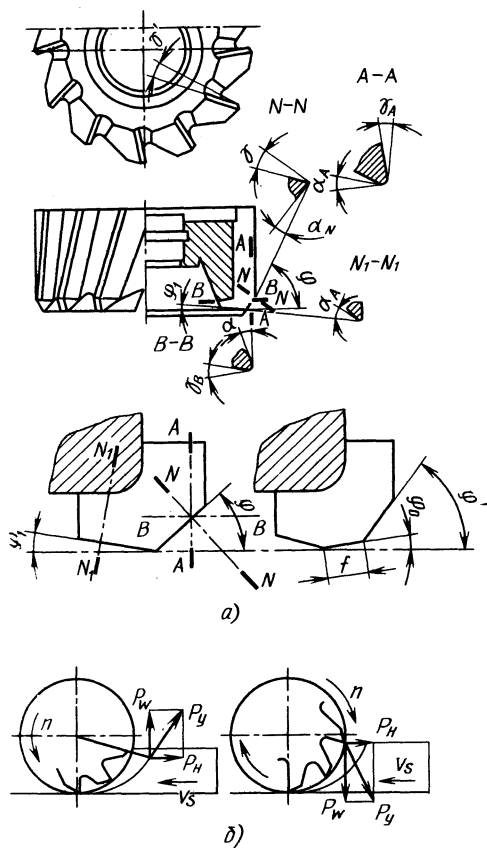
Конструкция торцевой фрезы (а); схемы заботы при встречном (б) и попутном фрезеровании (в)
